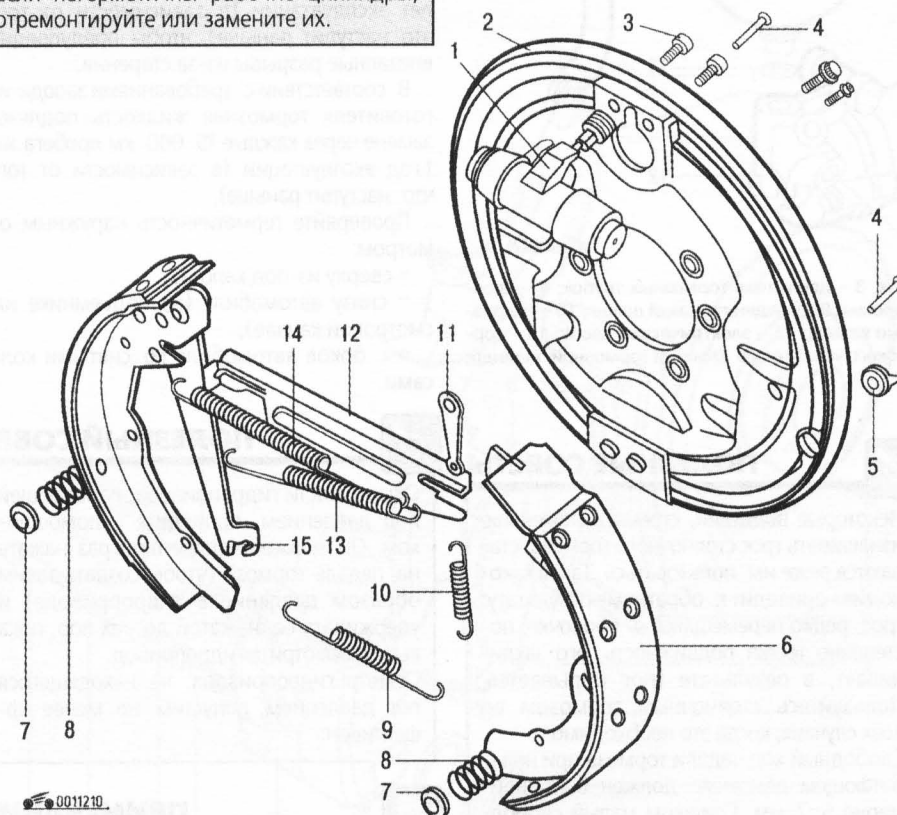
Барабанный тормозной механизм заднего колеса: 1 – рабочий тормозной цилиндр; 2 – тормозной щит; 3 – болт крепления тормозного цилиндра; 4 – штифт прижимной пружины; 5 – пробка смотрового отверстия; 6 – тормозная колодка; 7 – чашка; 8 – прижимная пружина; 9 – нижняя возвратная пружина; 10 – натяжная пружина клина; 11 – клин; 12 – распорная планка; 13 – верхняя возвратная пружина; 14 – стяжная пружина; 15 – рычаг стояночного тормоза
